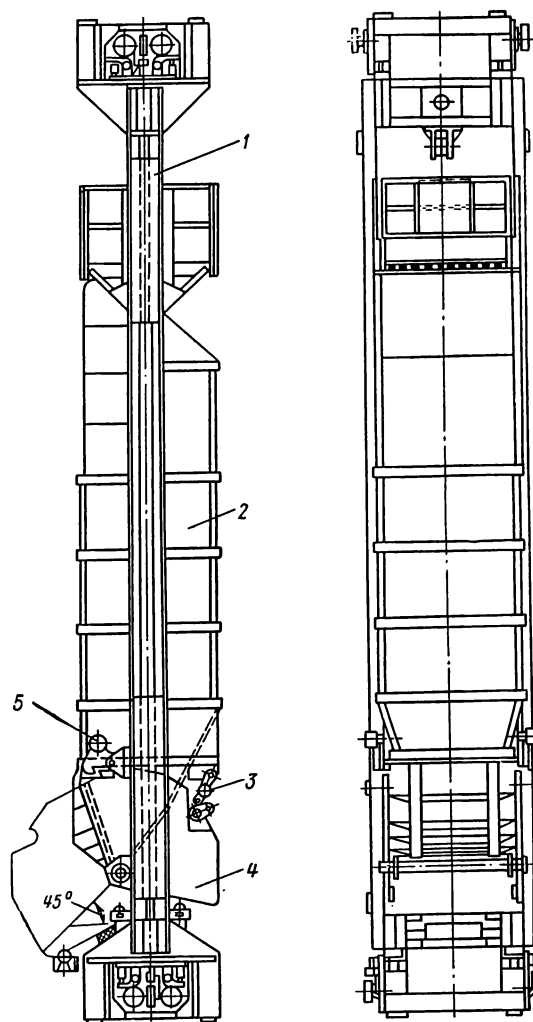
Общий вид породного скипа с неподвижным кузовом и клапанным затвором конструкции института Южгипрошахт:
